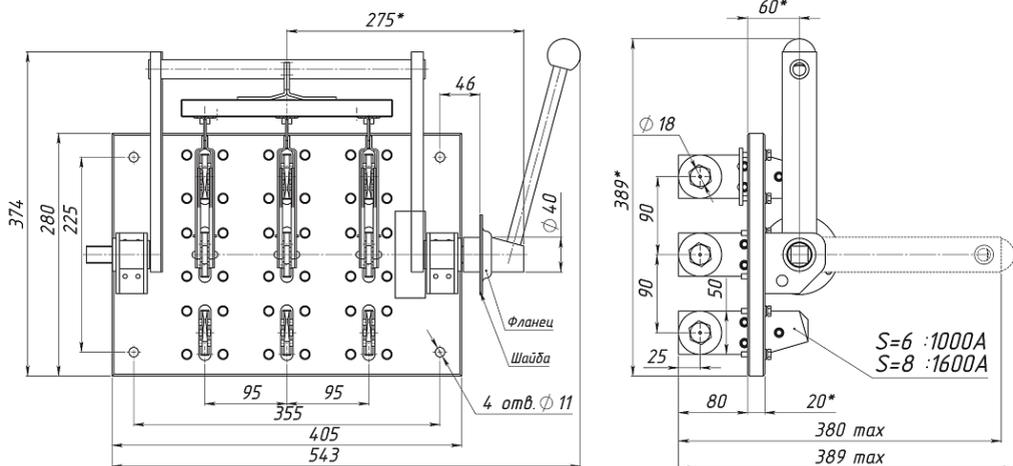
Разъединитель РЕ19-41(43)-72250-00 УХЛЗ на два направления с боковой смещенной рукояткой
